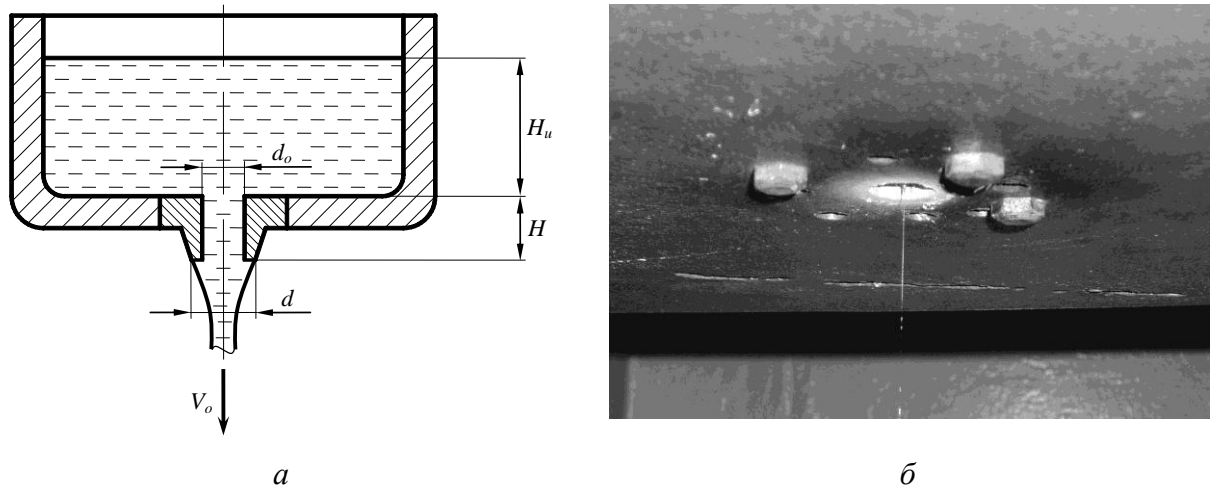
Схема та вигляд робочої зони установки для витягування алмазного волокна.
